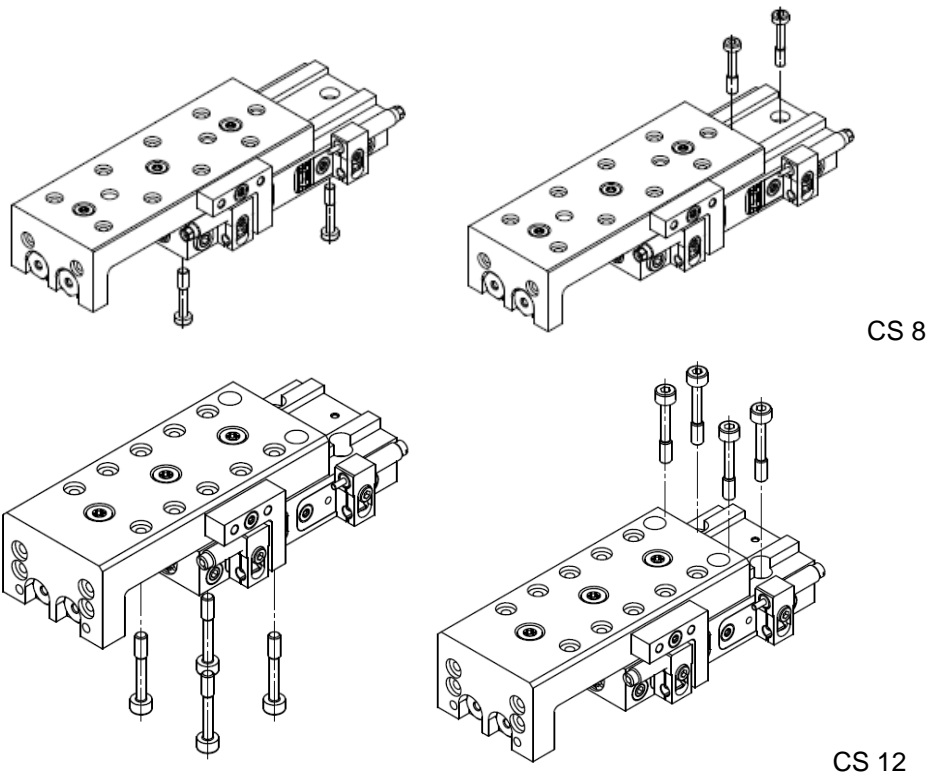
Montage Grundkörper von unten Montage Grundkörper durchgeschraubt
